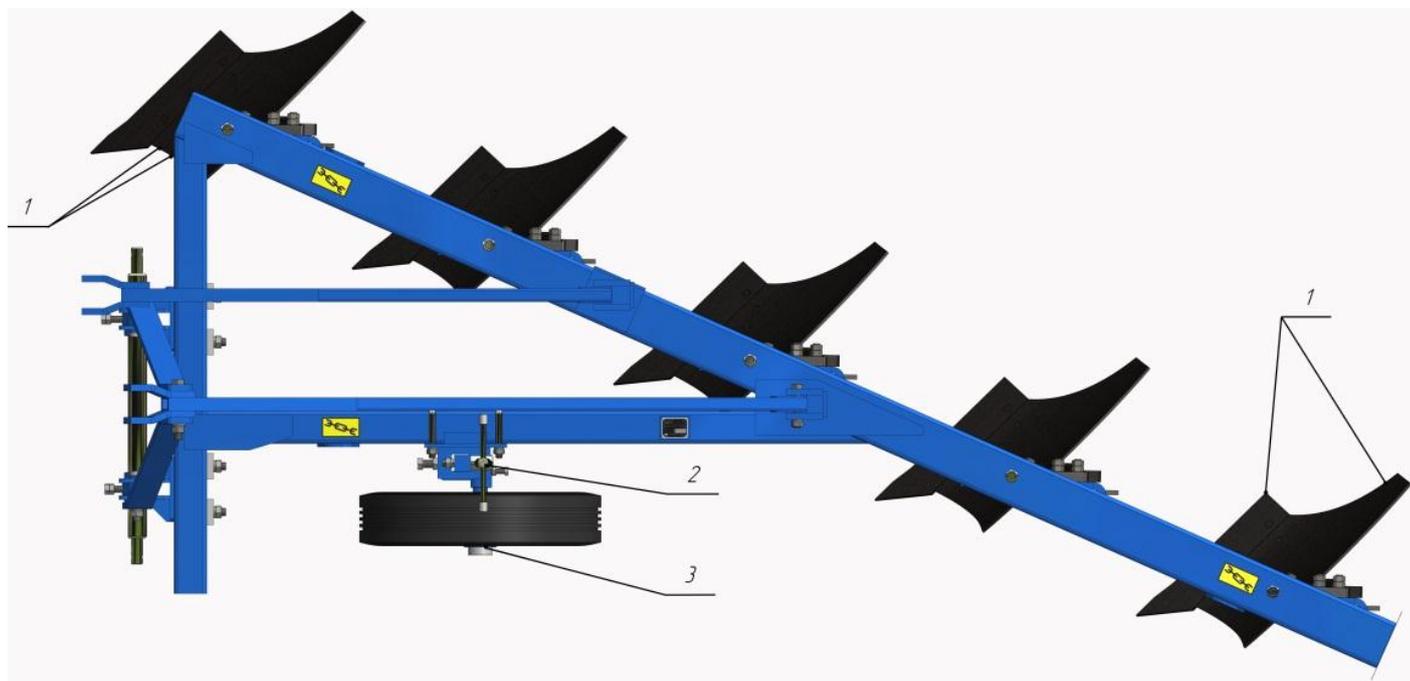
Схема смазки ПЛУ-5-35 ( см. табл.4)
